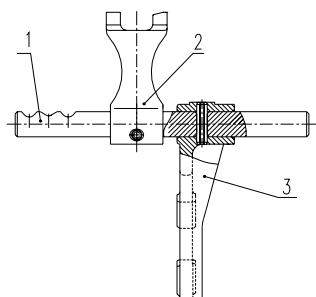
Вал вилки в сборе шестерни первой и второй передачи.
